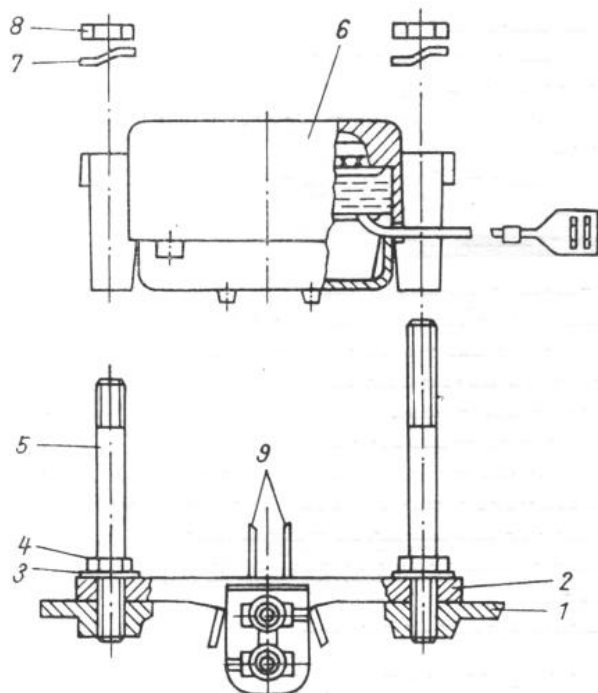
Montage des Spannungsreglers auf die Drehstromlichtmaschine
